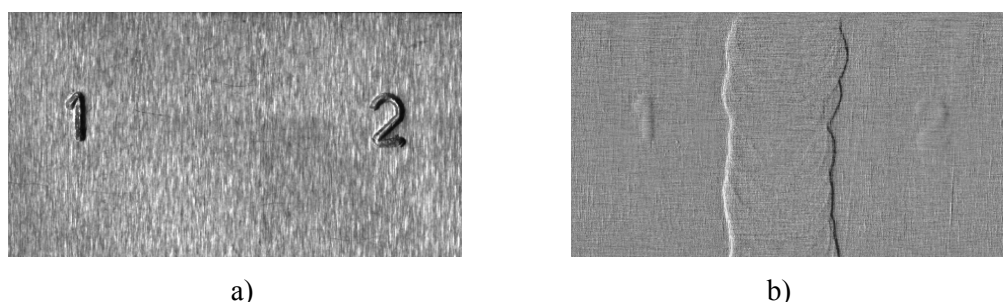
Изображение (а) и МО ВТ образ МГ (b) бездефектного сварного шва в нержавеющей стали.
